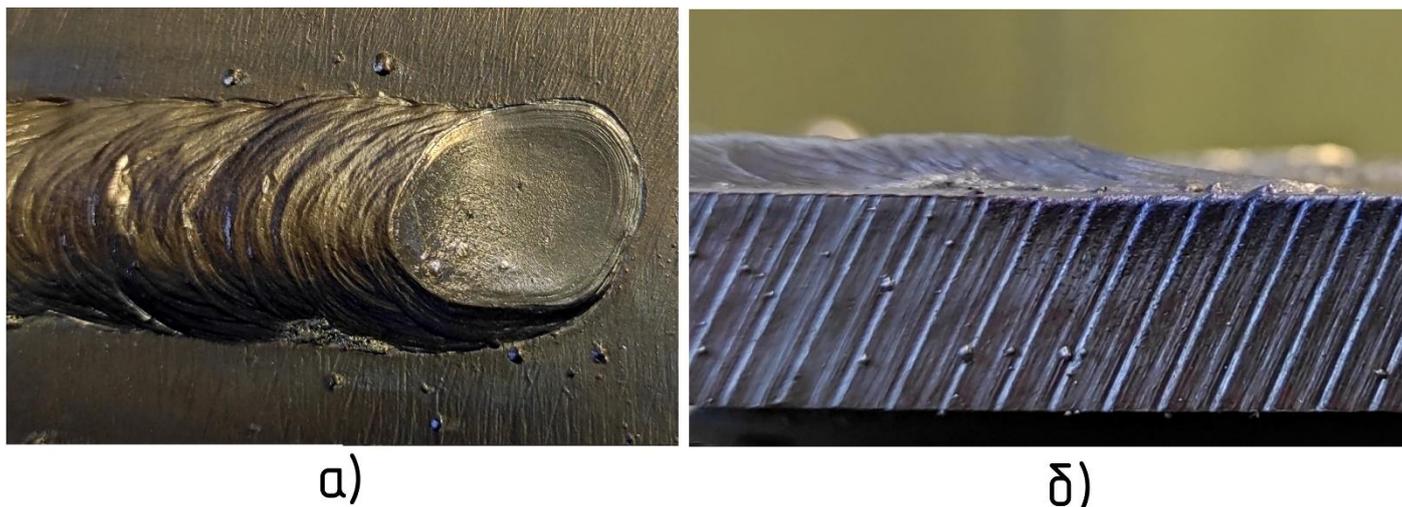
Форма кратера сварного шва, полученного резким обрывом дуги: а) – вид сверху; б) – вид сбоку.
